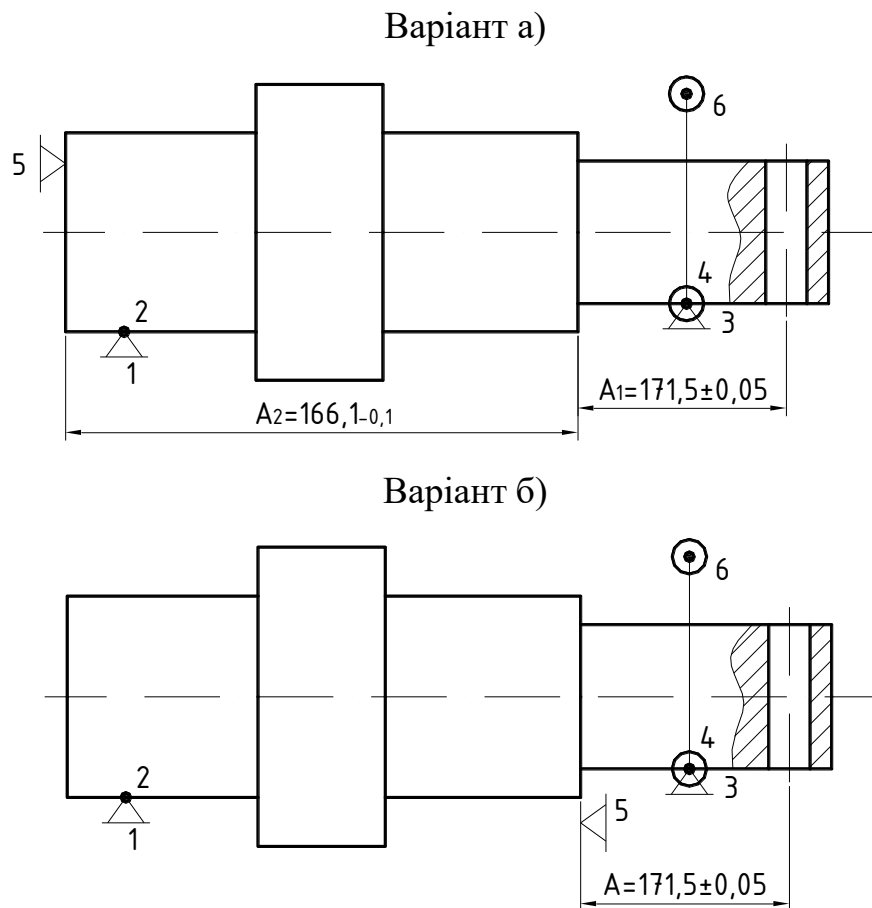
Схеми базування за обробки базового отвору 39
